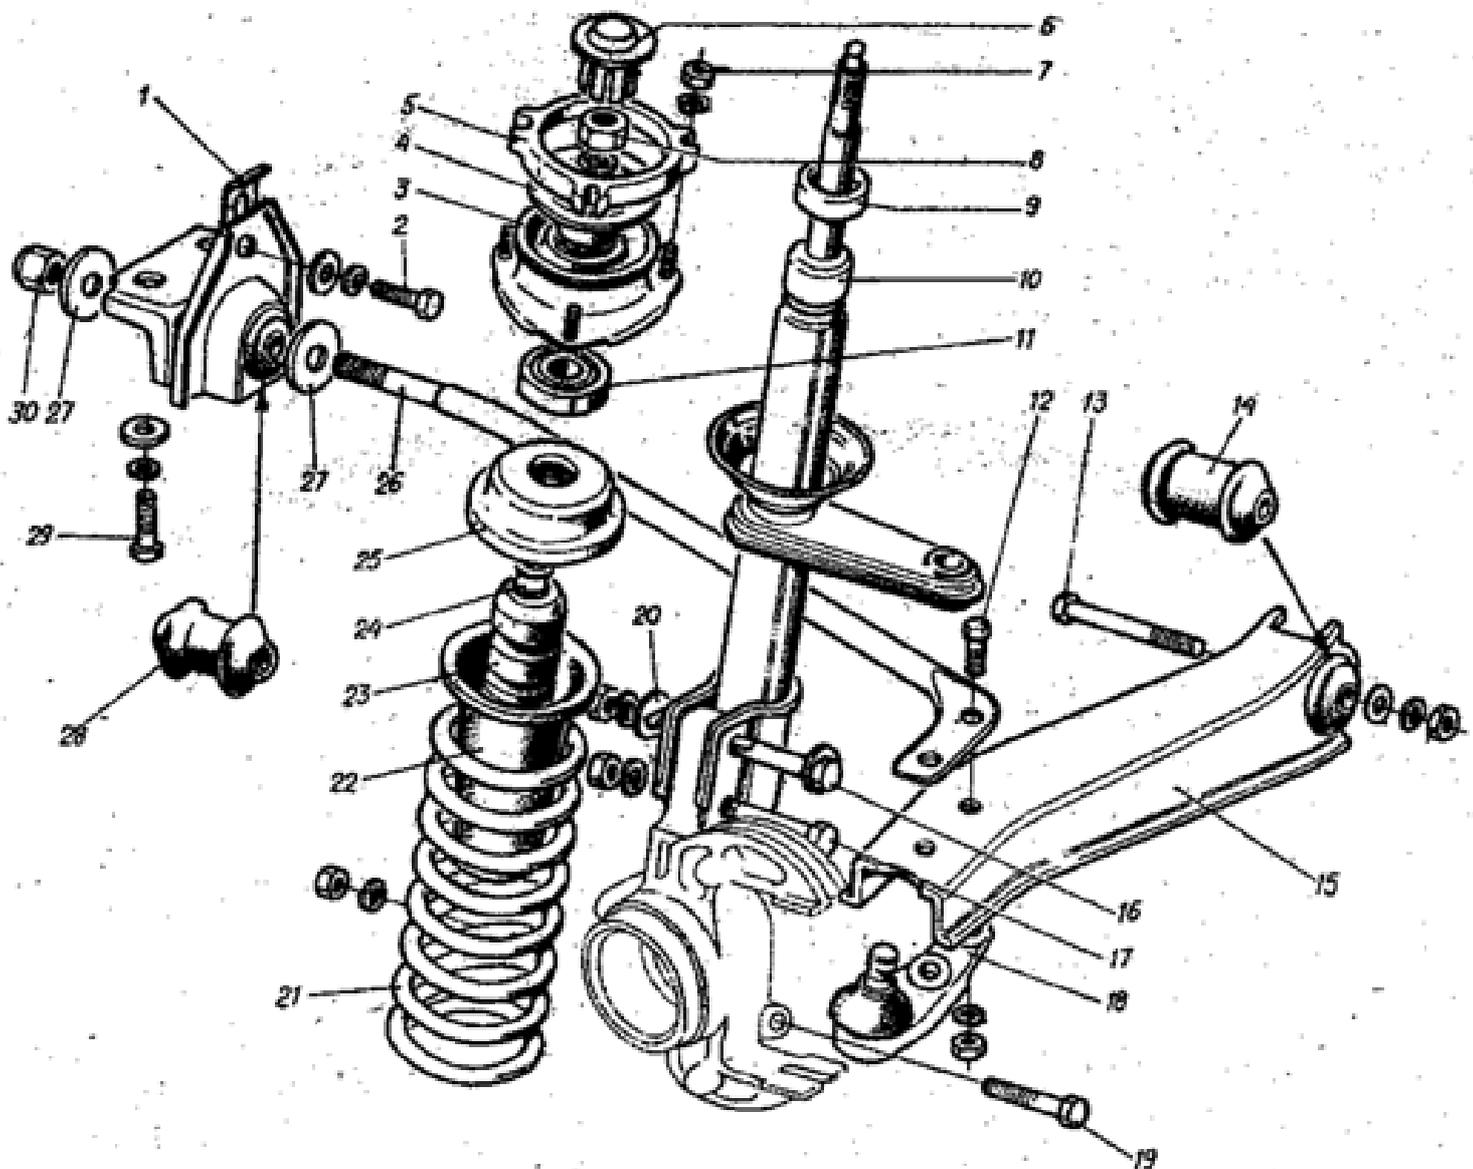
Детали передней подвески: 1 - прокладка компенсационная; 2, 29 - болт крепления кронштейна; 3 - опора стойки; 4 - ограничитель хода; 5 - прокладка; 6 - колпачок; 7 - гайка крепления верхней опоры; 8 - гайка крепления амортизатора; 9 - обойма буфера; 10 - амортизатор в сборе; 11 - подшпильник; 12 - болт крепления реактивной штанги к рычагу; 13 - болт крепления поперечного рычага; 14 - сайлентблок поперечного рычага; 15 - рычаг поперечный; 16 - болт регулировки угла развала колес и крепления амортизационной стойки; 17 - болт крепления амортизатора к поворотному кулаку; 18 - шарнир шаровой; 19 - болт клеммного соединения; 20 - шайба стопорная; 21 - пружина; 22 - чехол; 23 - буфер сжатия; 24 - втулка; 25 - чашка опорная; 26 - штанга реактивная; 27 - шайба; 28 - сайлентблок; 30 - гайка крепления реактивной штанги.
